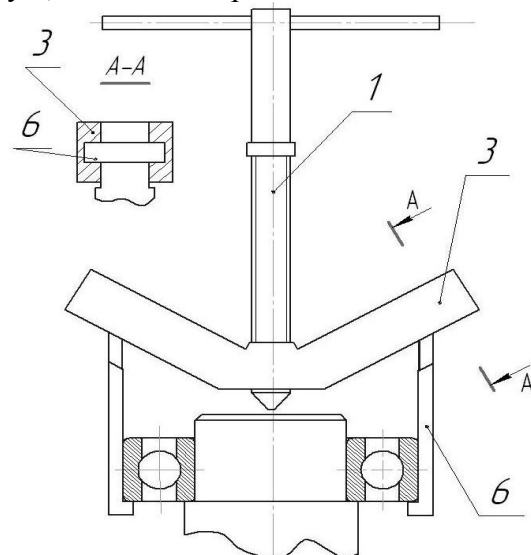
Схема демонтажу підшипника з валу знімачем з самозатискними лапами циліндричної форми
